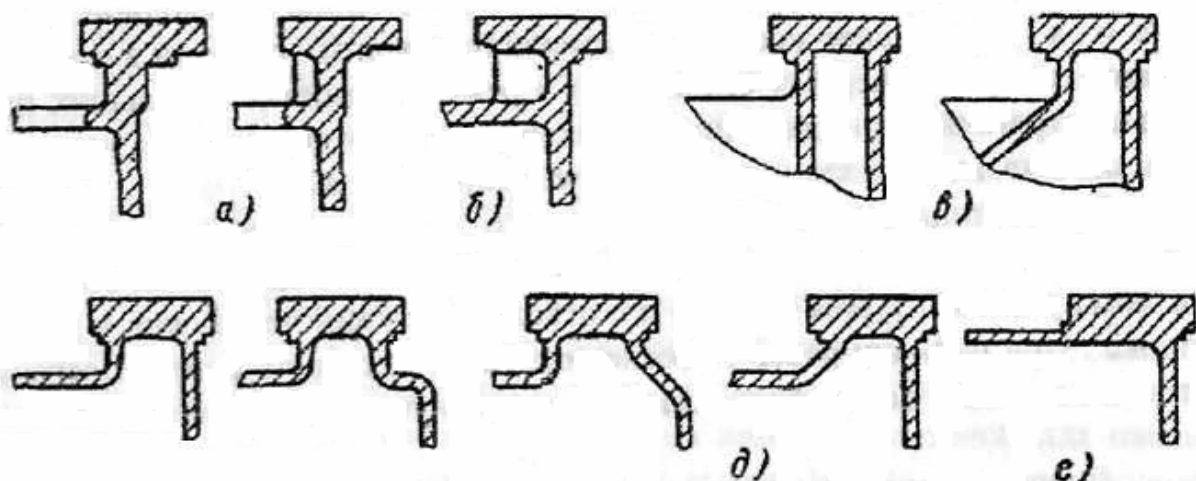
Конструктивные формы соединения направляющих к основной части станины
